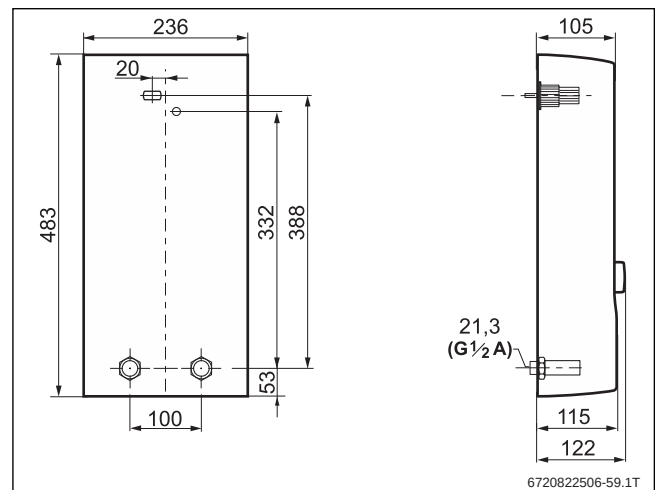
Abmessungen Tronic 8500 DESOAB (Maße in mm)
